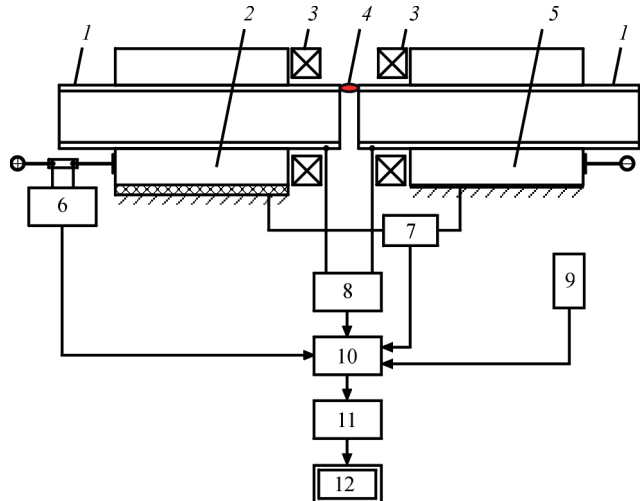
Блок-схема макету оцінки якості зварюваних з'єднань: 1 – зварювані труби; 2 – рухомий затискний пристрій; 3 – елементи магнітної системи; 4 – стовп електричної дуги; 5 – нерухомий затискний пристрій; 6 – датчик струму; 7 – датчик положення; 8 – датчик падіння напруги на зварювальній дузі; 9 – датчик вимірювання абсолютного тиску гідравлічної системи; 10 – нормуючий інструментальний підсилювач (з ФНЧ $F_{зр} = 100$ Гц); 11 – приймаючий АЦП; 12 – промисловий комп'ютер
